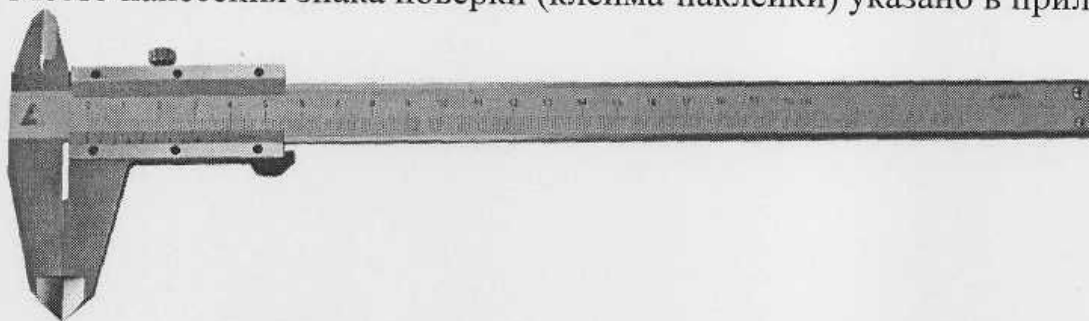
Внешний вид штангенциркулей ШЦ-I
